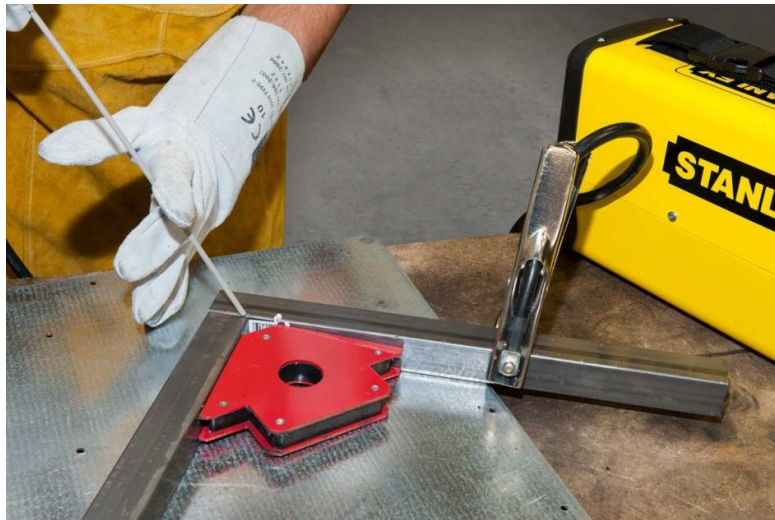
soudage à l'arc en électrode enrobée cadre support
